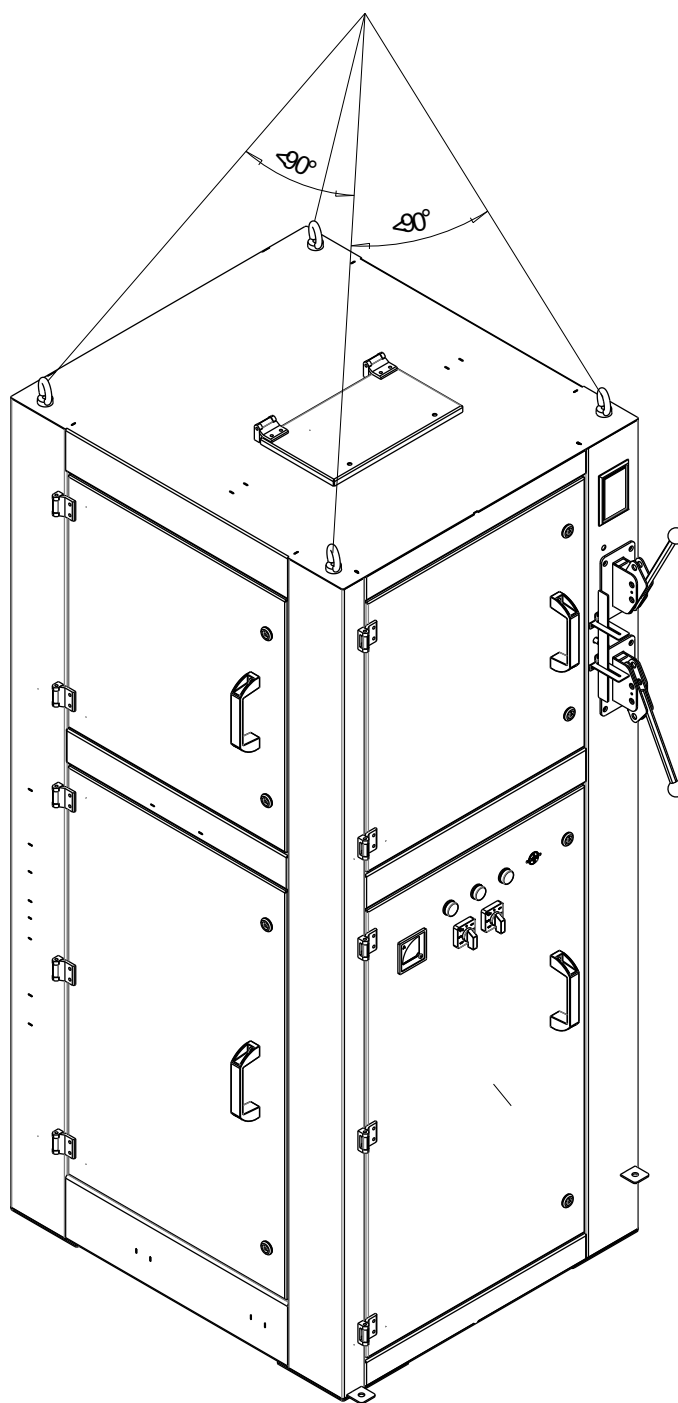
Схема строповки шкафа КРУ-2КВЭ-6
